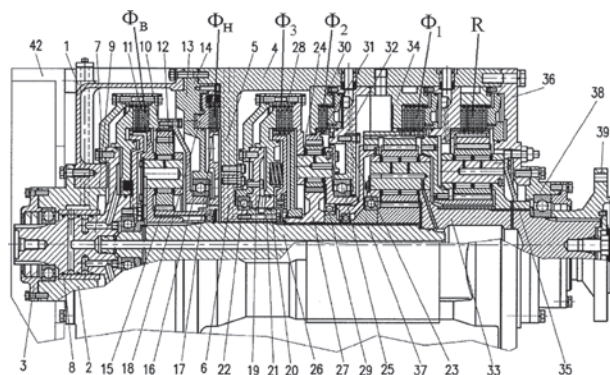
Конструкция коробки передач GMT карьерного самосвала БелАЗ-75571 [10, 12]
